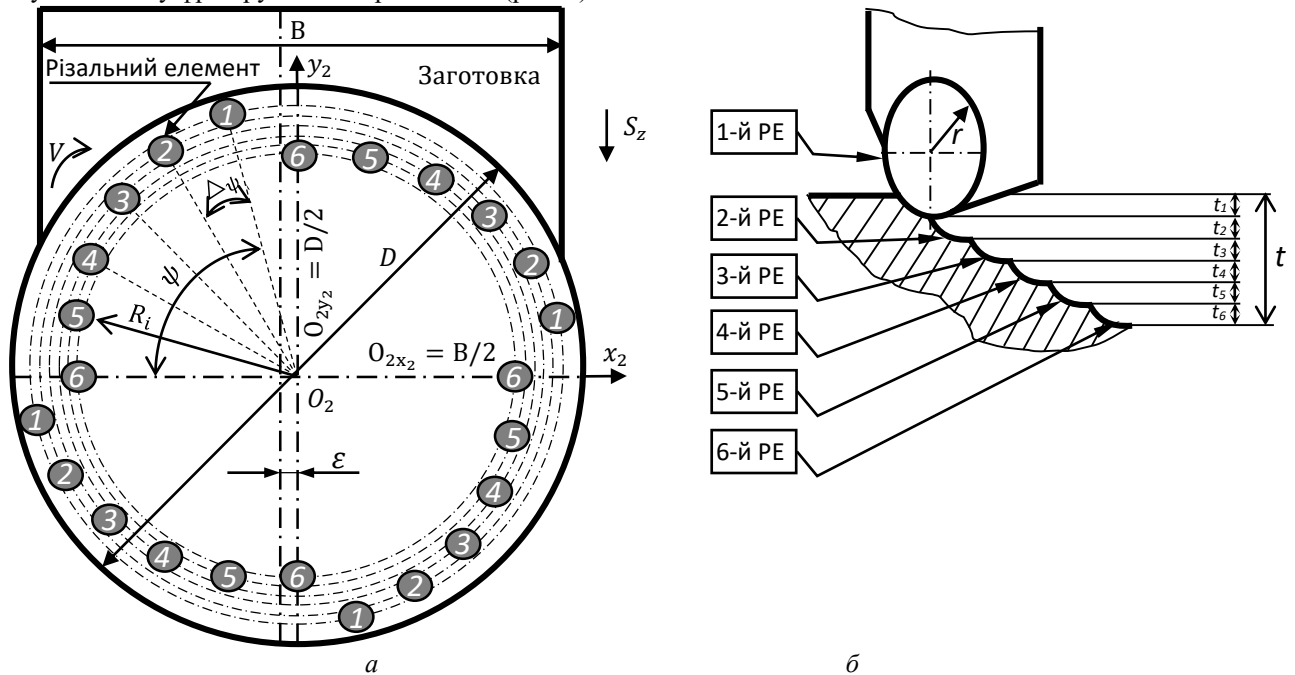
Схема побудови математичної моделі: а) розташування торцевої ступінчастої фрези відносно заготовки; б) схема різання
